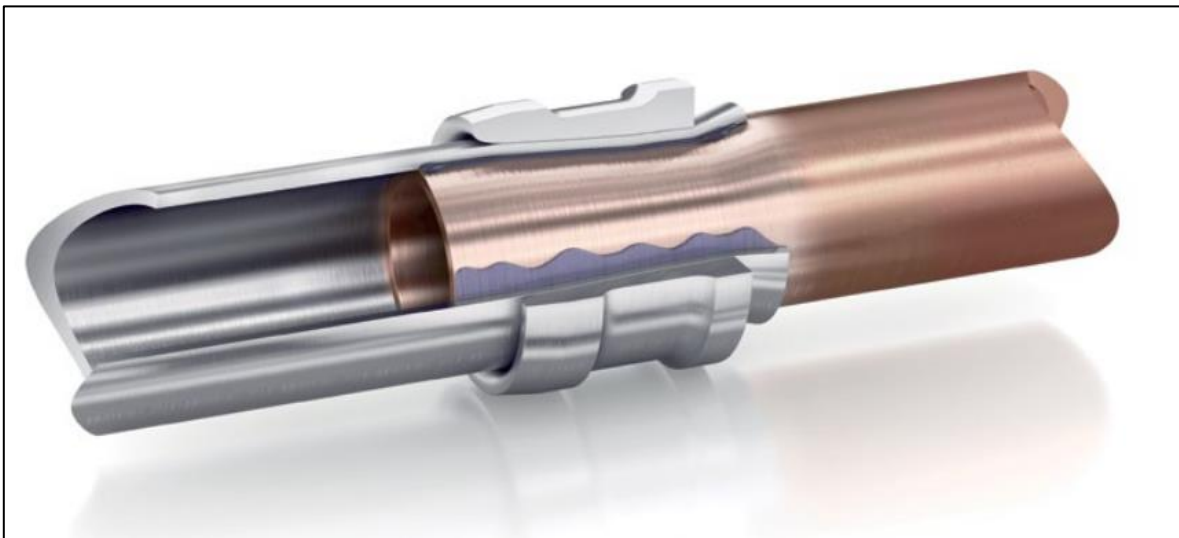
Vista seccionada de unión mediante soldadura LOKRING. Fuente: vulkan.com
